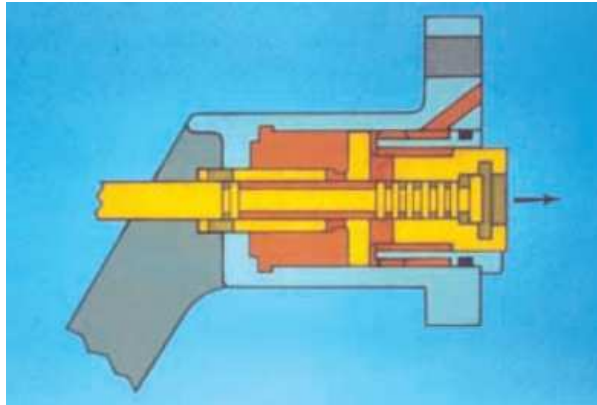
Carrete de la válvula en posición de "CORTE DE COMBUSTIBLE"
